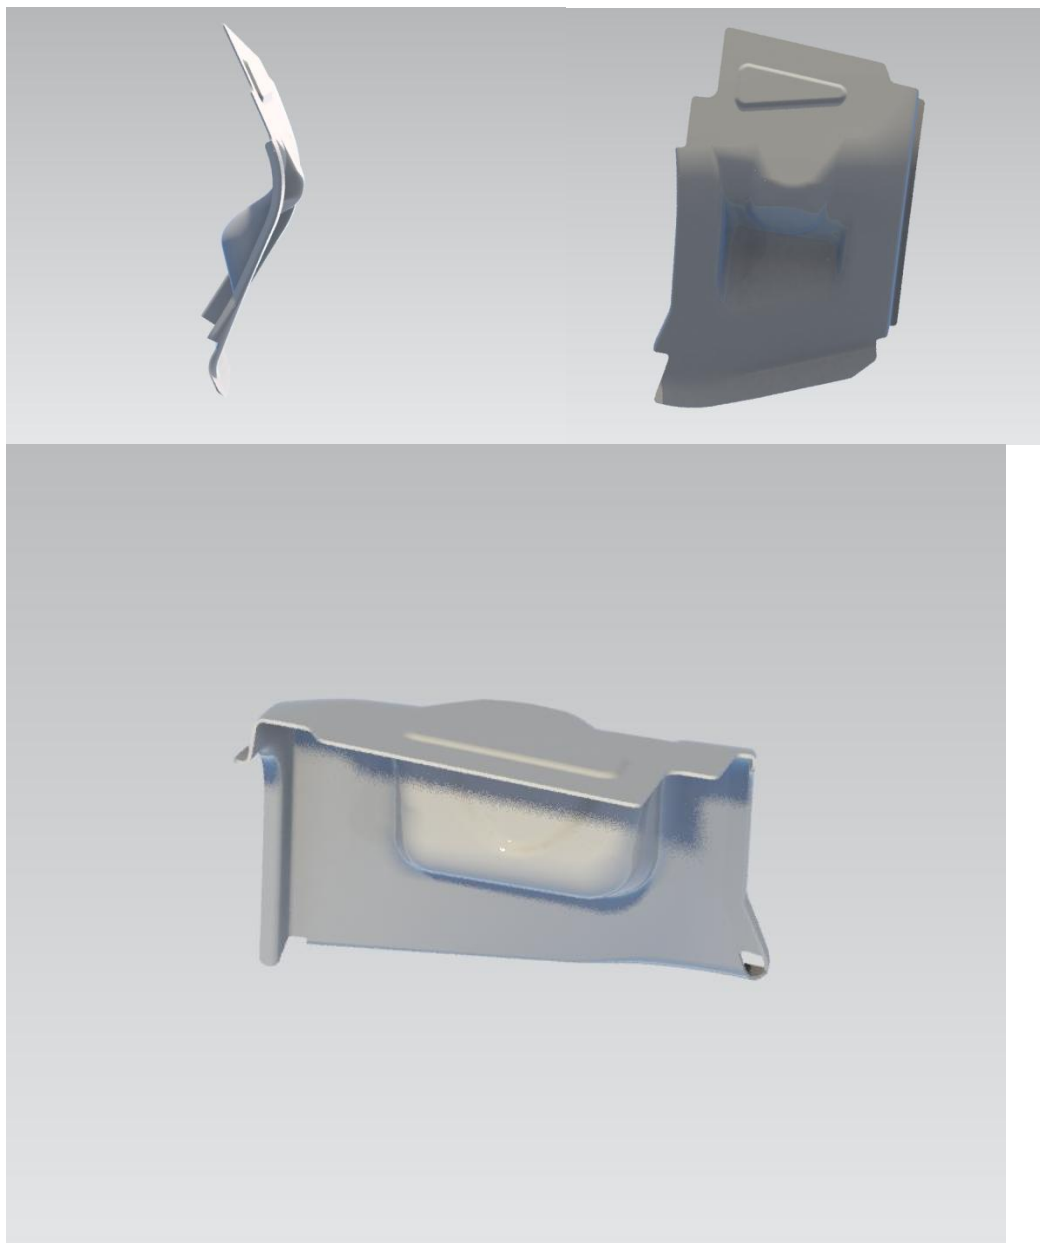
Рендер усилителя чашки крепления амортизатора
